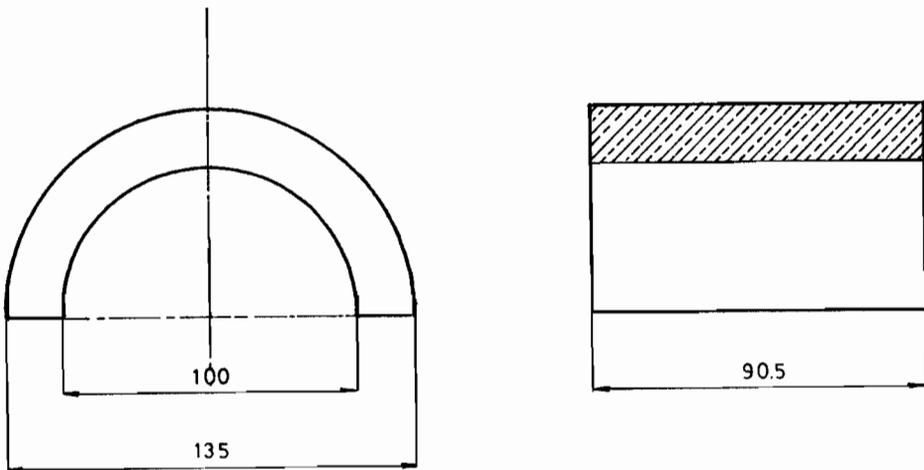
DIMENSIONES DEL BOCIN DEL EJE
